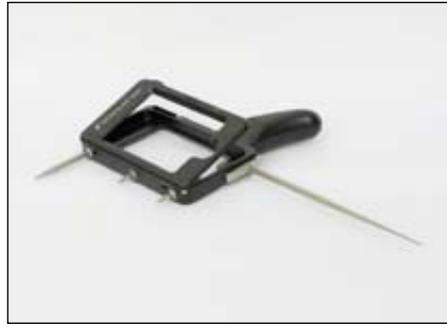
Der Integral für joystick-geführtes Auftragschweißen oder CNC Bearbeitung
